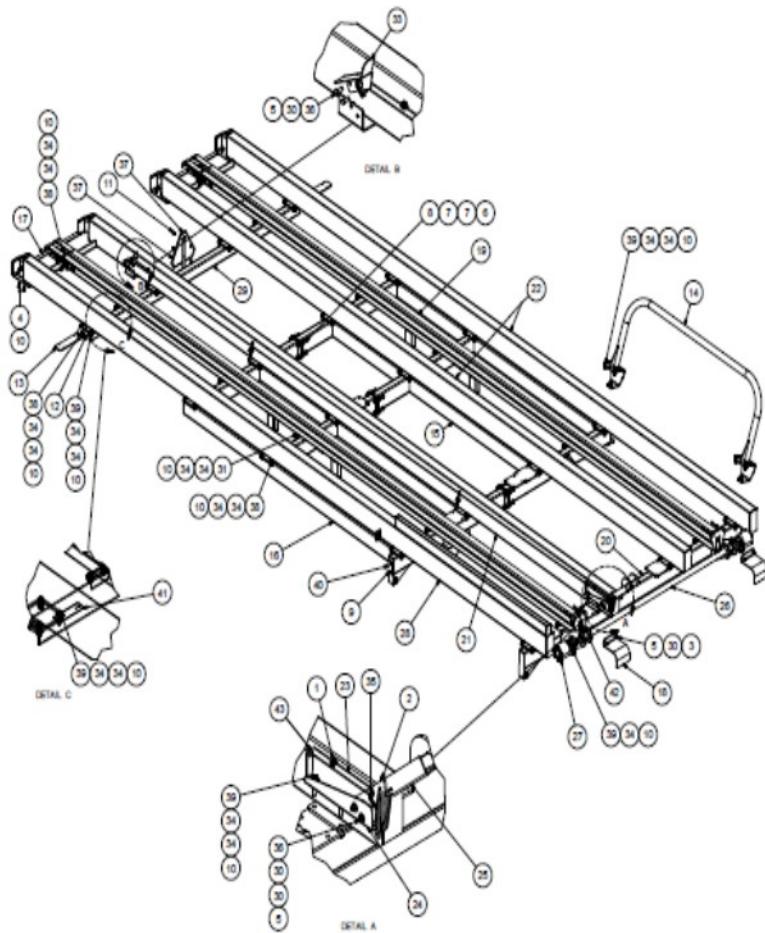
Чертеж сборки рамы тележки – 815621
